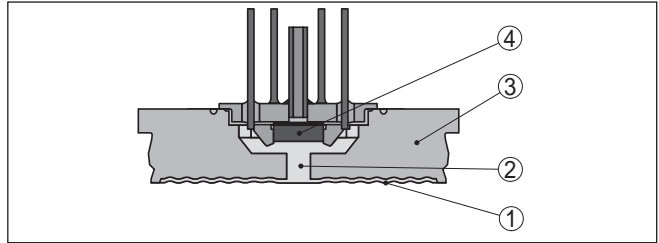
Estrutura do sistema de medição com elemento sensor piezo-resistivo
